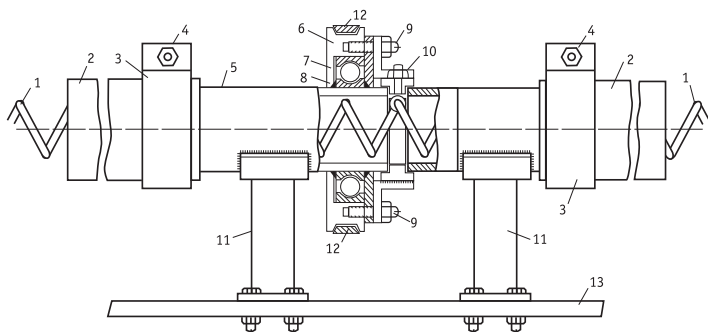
Деталь крепления спирали при двусторонней работе установки: 1 – спираль; 2 – шланг; 3 – хомут; 4 – болт; 5 – патрубок; 6 – шкив; 7 – подшипник; 8 – сальники; 9 – болт; 10 – болт с ушком; 11 – стойки; 12 – ременная передача; 13 – станина.
